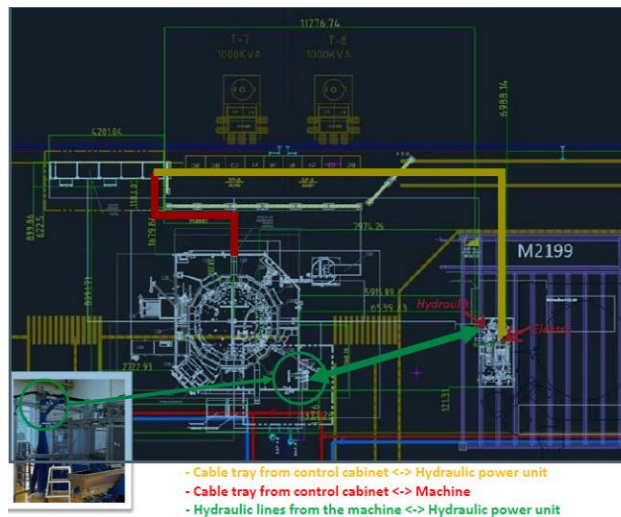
Layout de la vista preliminar de la Máquina VMR y cableado de control, control y línea hidráulica (Programa SolidWorks).
